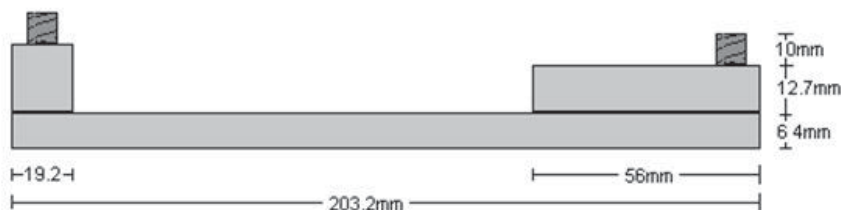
Diseño de placas que actuaron como base de las juntas a unir
